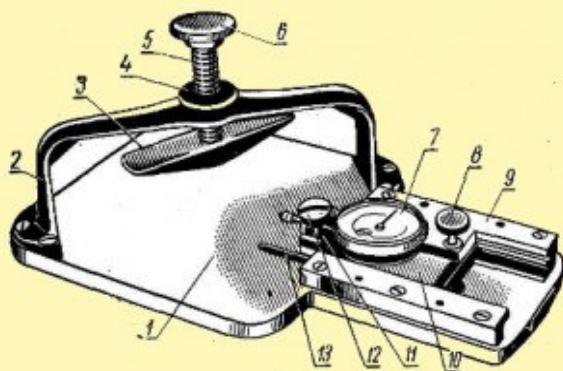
Прибор КИ-1223 для измерения радиального зазора в подшипниках качения.
